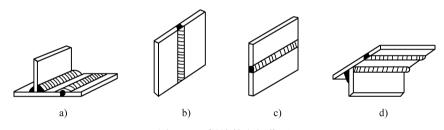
焊缝的空间位置 a) 平焊缝 b) 立焊缝 c) 横焊缝 d) 仰焊缝
